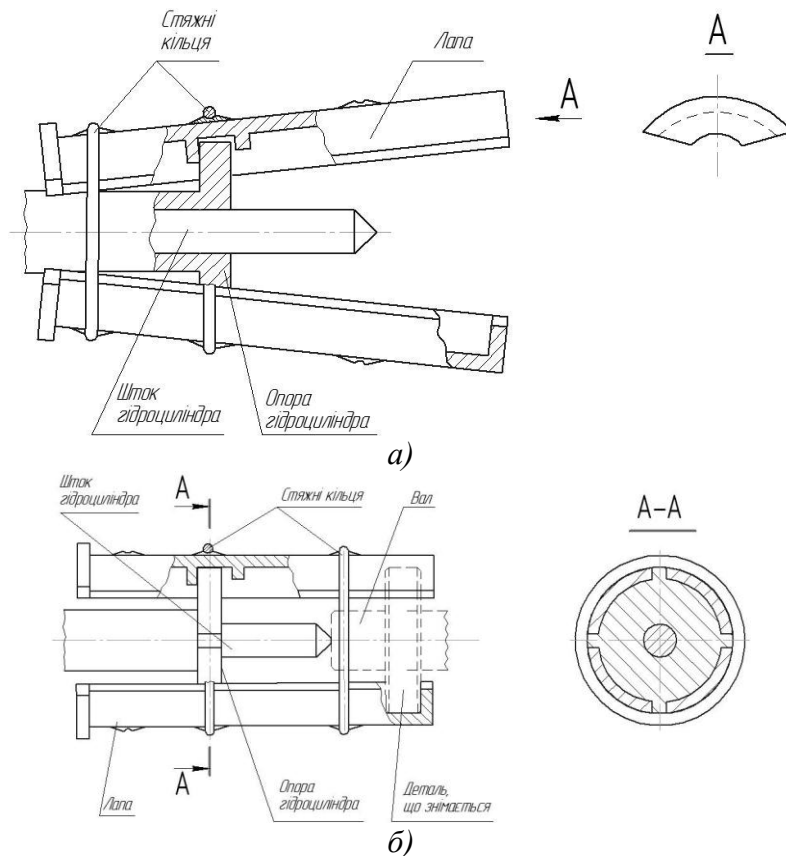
Знімач підшипників з коливними легкоз'ємними лапами циліндричної форми.
